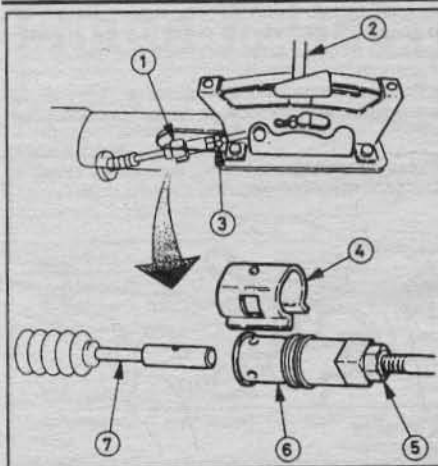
Детали регулировки троса переключения: 1 - защелка, 2 - рычаг, 3 - контргайка, 4 - защелка, 5 - контргайка, 6 - регулятор длины, 7 - трос.
